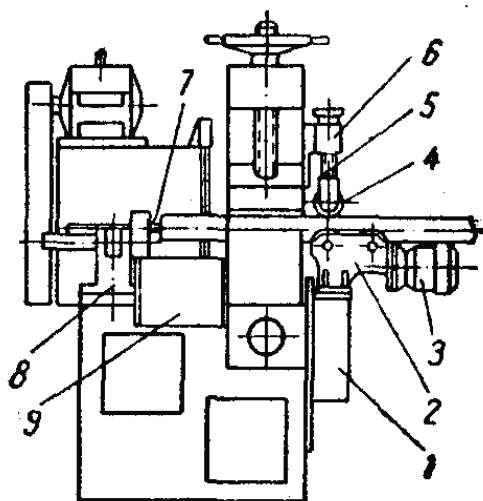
Схема модернизации фрезерно - отрезного станка мод. 8А66
